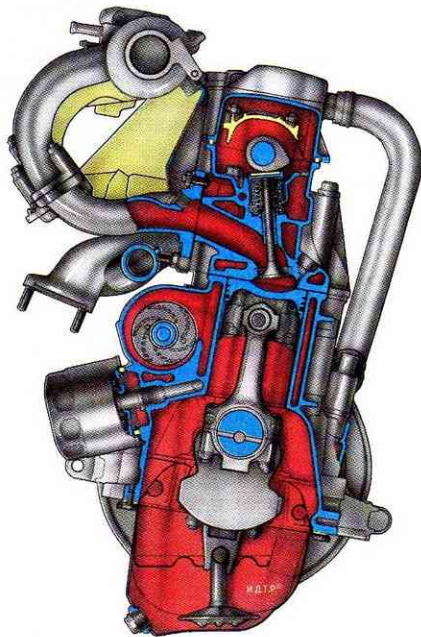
Поперечный разрез двигателя ВАЗ-2111
